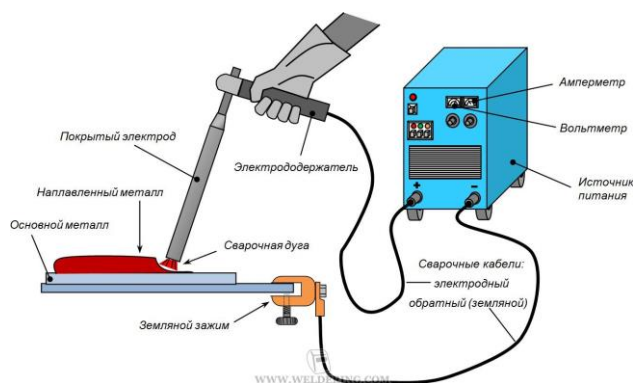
Схема выполнения ручной дуговой сварки
